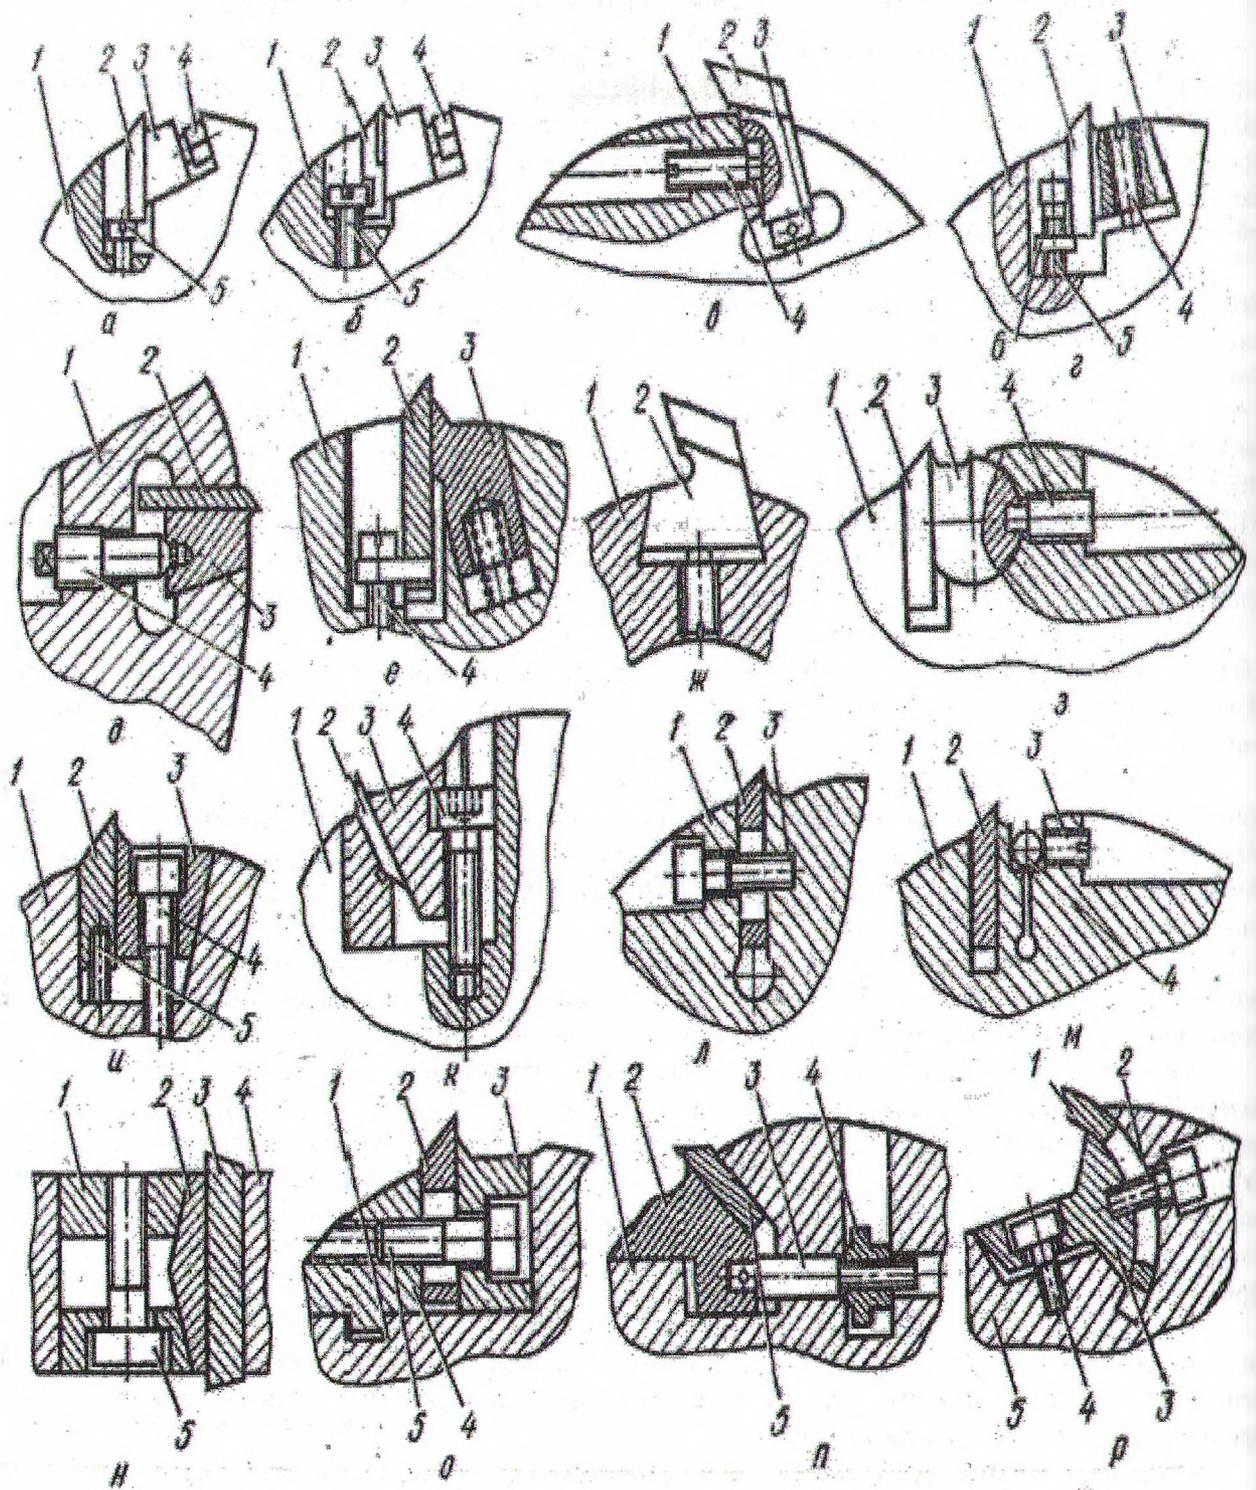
Конструктивные решения крепления режущих элементов сборных фрез: а, б, е – распорным клином; г, д, е, ж – выжимным клином; э – клином с цилиндрической поверхностью; и, к – затяжным клином; л, м – клеммовым креплением; н – для фрез небольшой ширины; о – сборная конструкция ножевого вала; п – с прижимным элементом; р – дугового реза
